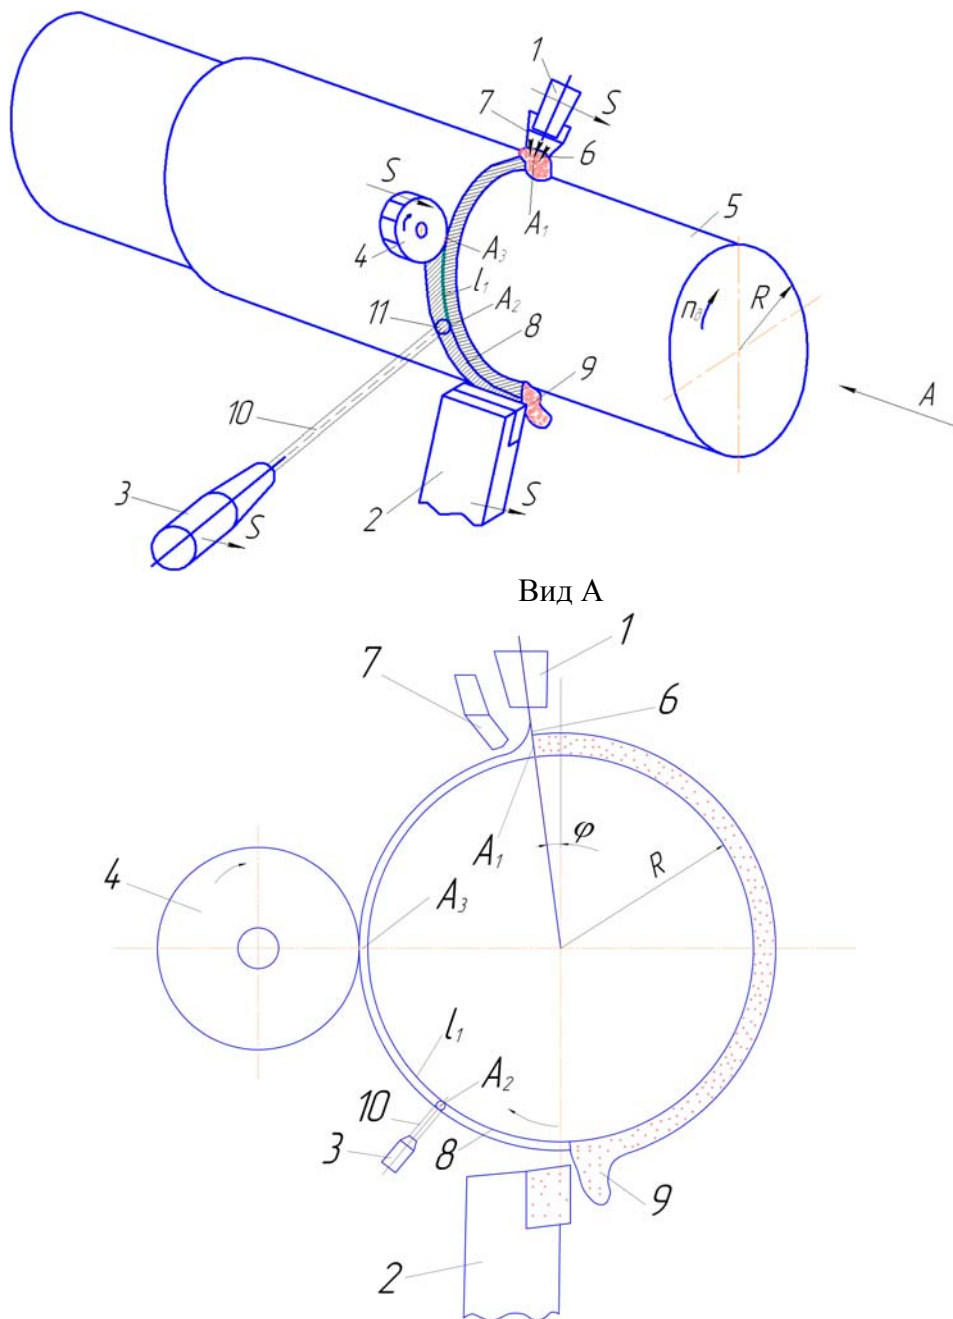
Схема наплавки металлоемкой детали с одновременным подогревом и механической обработкой металлопокрытия
